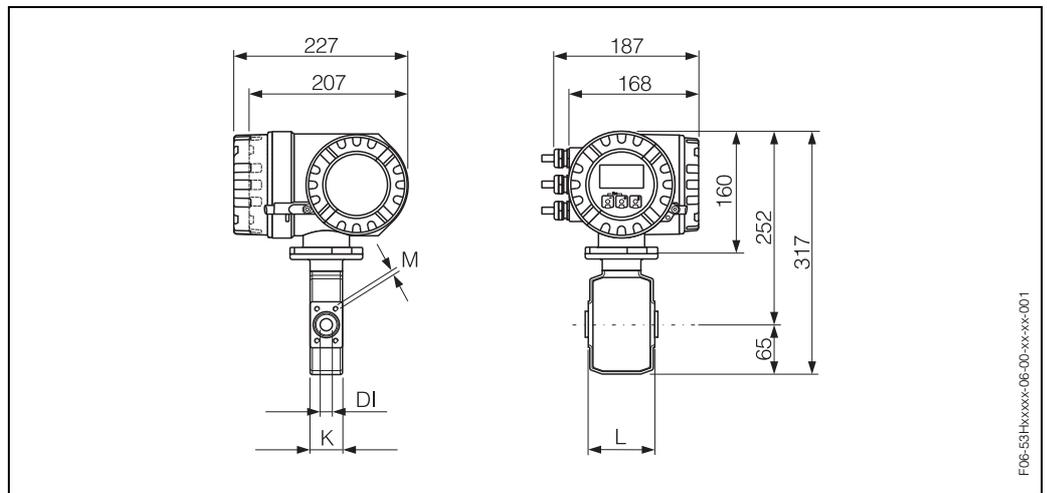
Abmessungen Promag H / DN 2...25 (Kompaktausführung, Aluminium-Feldgehäuse)
